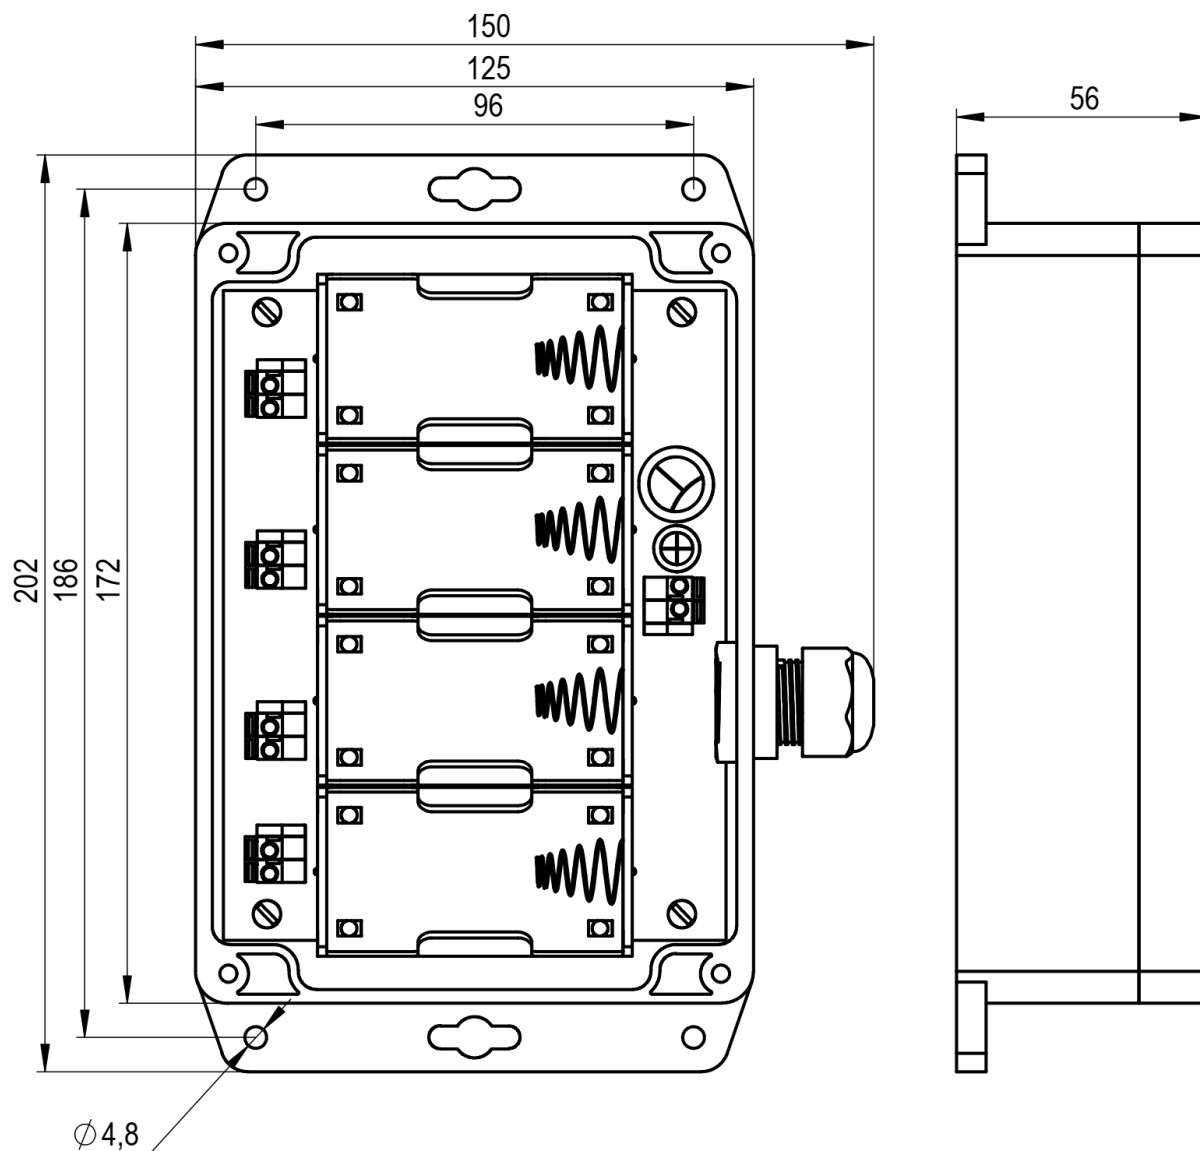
Габаритные и установочные размеры блока батарейного питания ПБ-4
